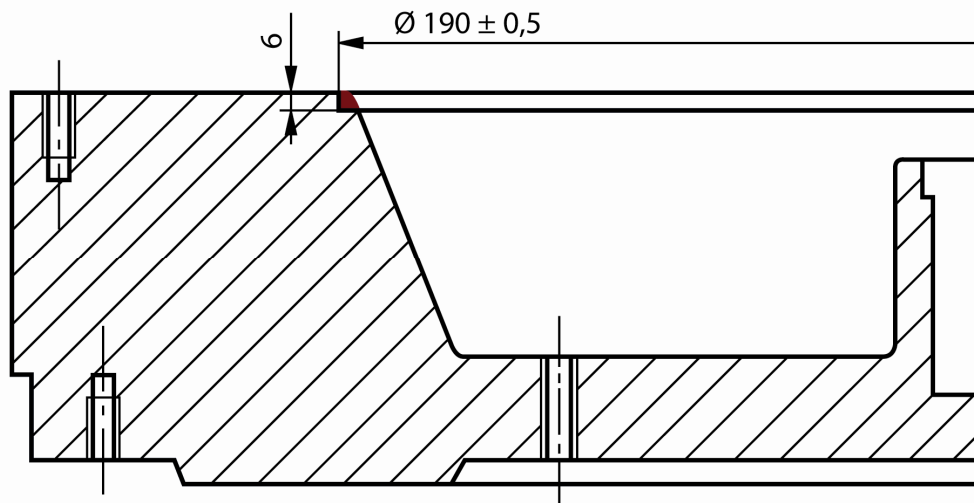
Schwungrad / Flywheel / Volant moteur / Volantes del motor \varnothing 190 mm - 6 mm / Tiefe / Depth / Profondeur / Profundidad
